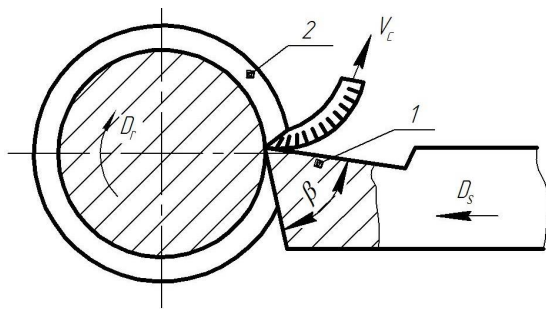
Схема різання: 1 – лезо інструмента; 2 – оброблювана заготівка; β – кут загострення леза
